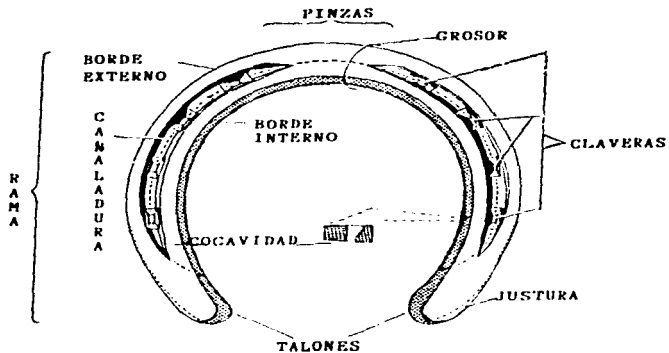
PRINCIPALES PARTES DE UNA HERRADURA.
